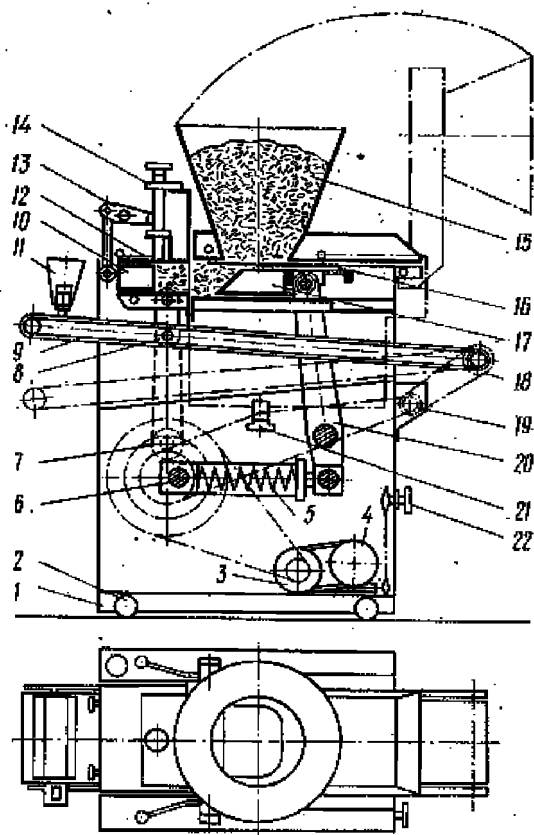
Тістоподільна машина «Кооператор»: 1 – станина; 2 – ролики; 3 – редуктор; 4 – двигун; 5 – пружинний демпфер; 6 – головний вал; 7 – диски з ексцентричними пальцями; 8 – шатун; 9 – стрічковий транспортер; 10 – прямокутні поршні; 11 – посипач борошна; 12 – подільна головка; 13 – виштовхувальний ричаг; 14 – механізм регулювання маси заготовки; 15 – приймальна воронка; 16 – заслінка; 17 – нагнітальний поршень; 18 – ланцюг; 19 – зірочка; 20 – ричаг; 21 – масляний насос; 22 – маховик регулювання частоти двигуна.
